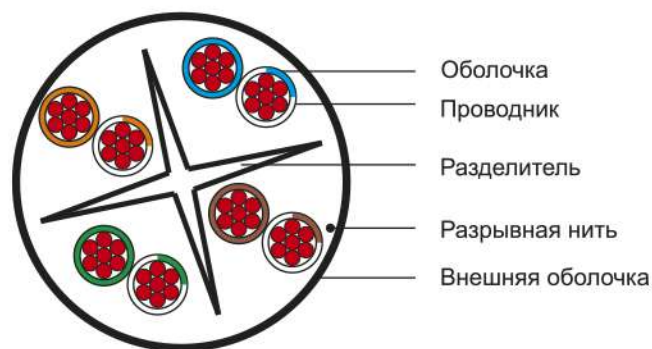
Конструкция кабеля типа U/UTP с многопроволочными жилами
